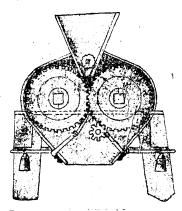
Плющильные цилиндры для раздавливанія сёмянъ въ мязгу. Сверху воронка, внутри ея зубчатое колесо. Внизу справа и слёва двъ скребки съ рычагами и противовъсами. Нижнею зубчаткою приводится въ движеніе одинъ изъ валовъ п шкивомъ валикъ въ воронкъ.
